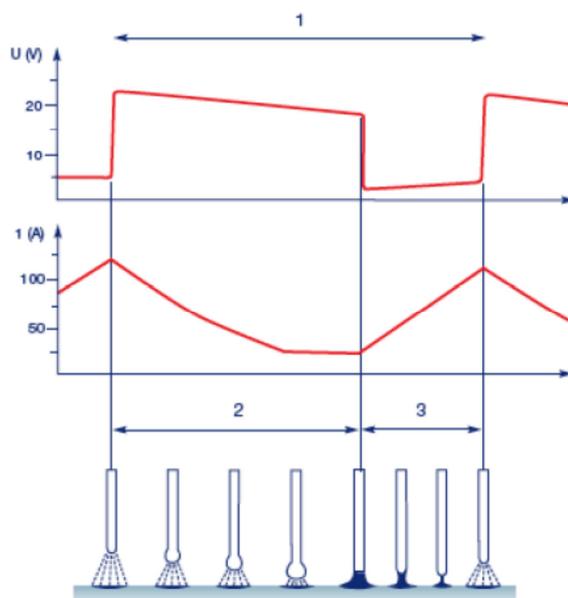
На конце электродной проволоки формируется капля расплавленного металла. Когда она становится достаточно крупной, происходит ее контакт со сварочной ванной и дуговой промежуток замыкается. В этот момент ток сварки резко повышается, и капля отделяется от проволоки. Дуга зажигается снова. При этом происходит образование некоторого количества сварочных брызг, связанное с резкими повышениями сварочного тока в момент замыкания дугового промежутка.
